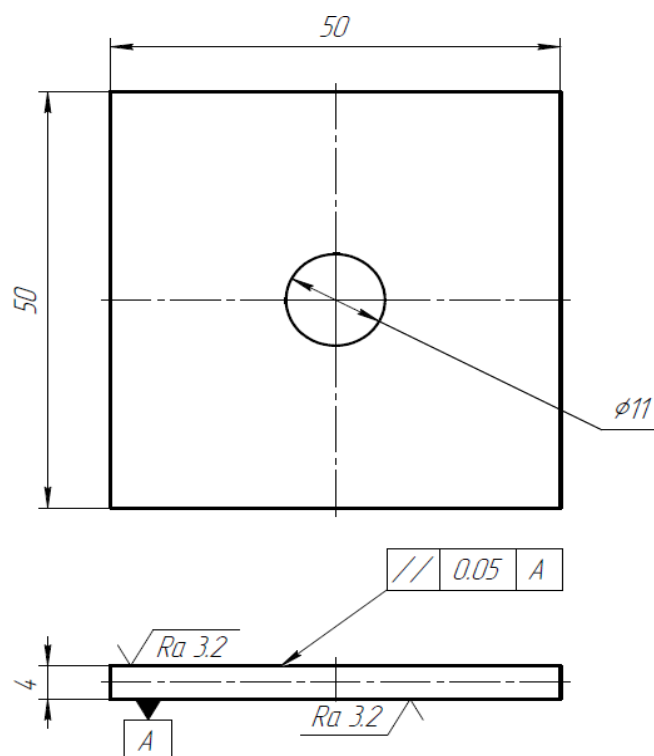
Геометрия и основные размеры образца для испытаний на сдвиг
